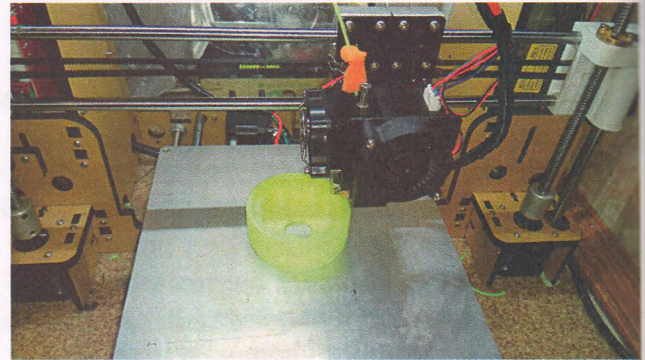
Изготовление профильного зубчатого венца на 3D-принтере
